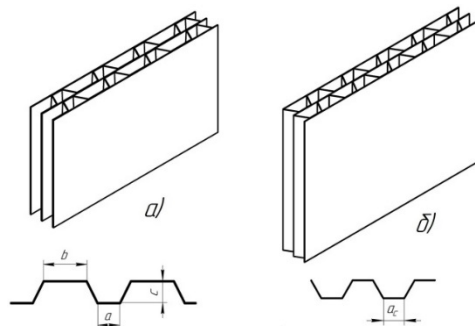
а) Новая схема наполнителя; б) Базовая схема наполнителя
